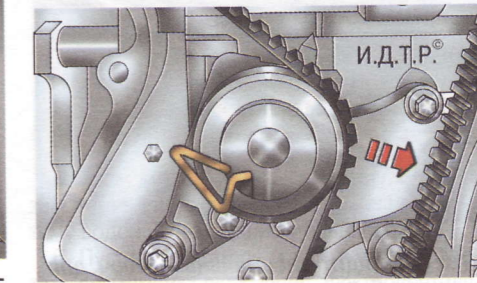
Ослабление натяжения ремня привода газораспределительного механизма
